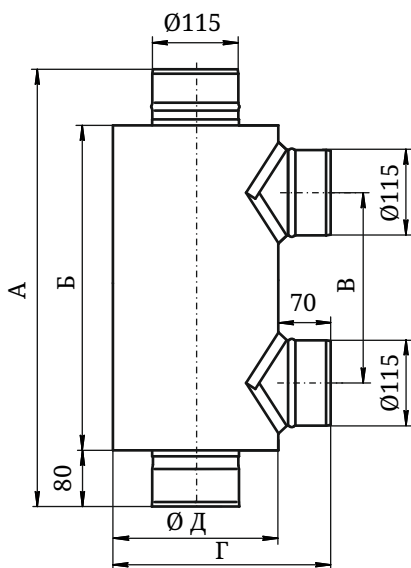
Отопитель натрубный для обогрева одного смежного помещения
